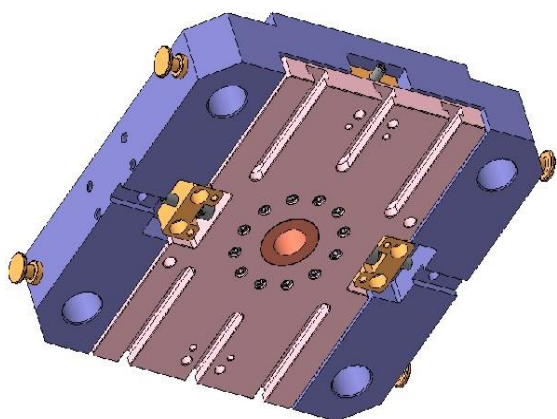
Універсальний механічний компенсатор для кривошипного преса-автомата з нижнім приводом номінальним зусиллям 400 кН
